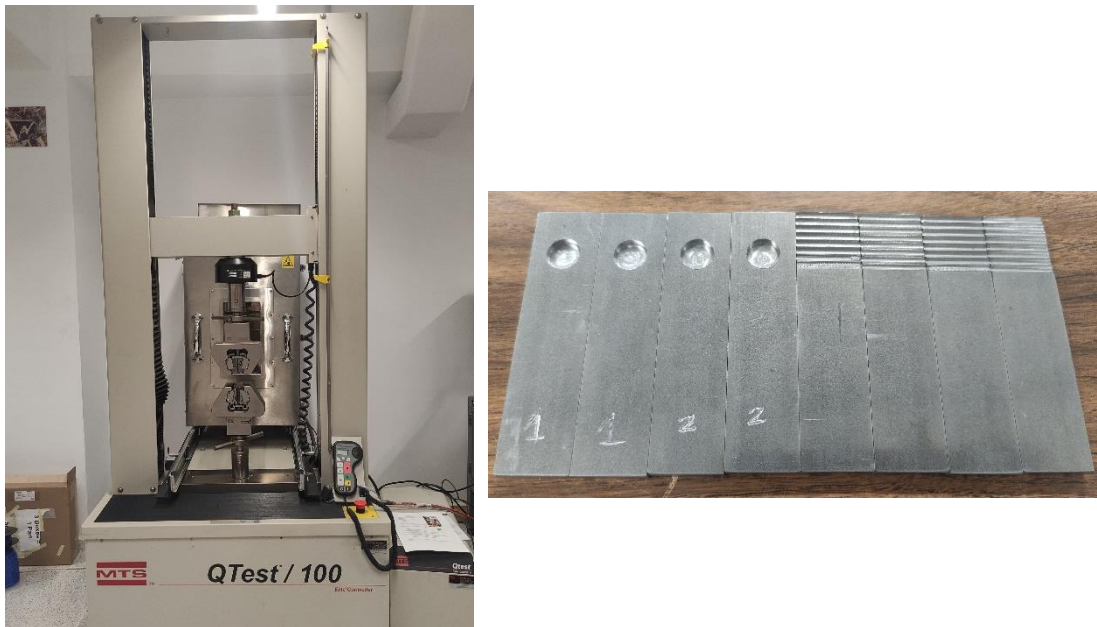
a) Máquina de ensayo universal; b) Bases fabricadas para alojar el conjunto disco-disco adherido y colocarlas en la máquina de ensayo universal.
